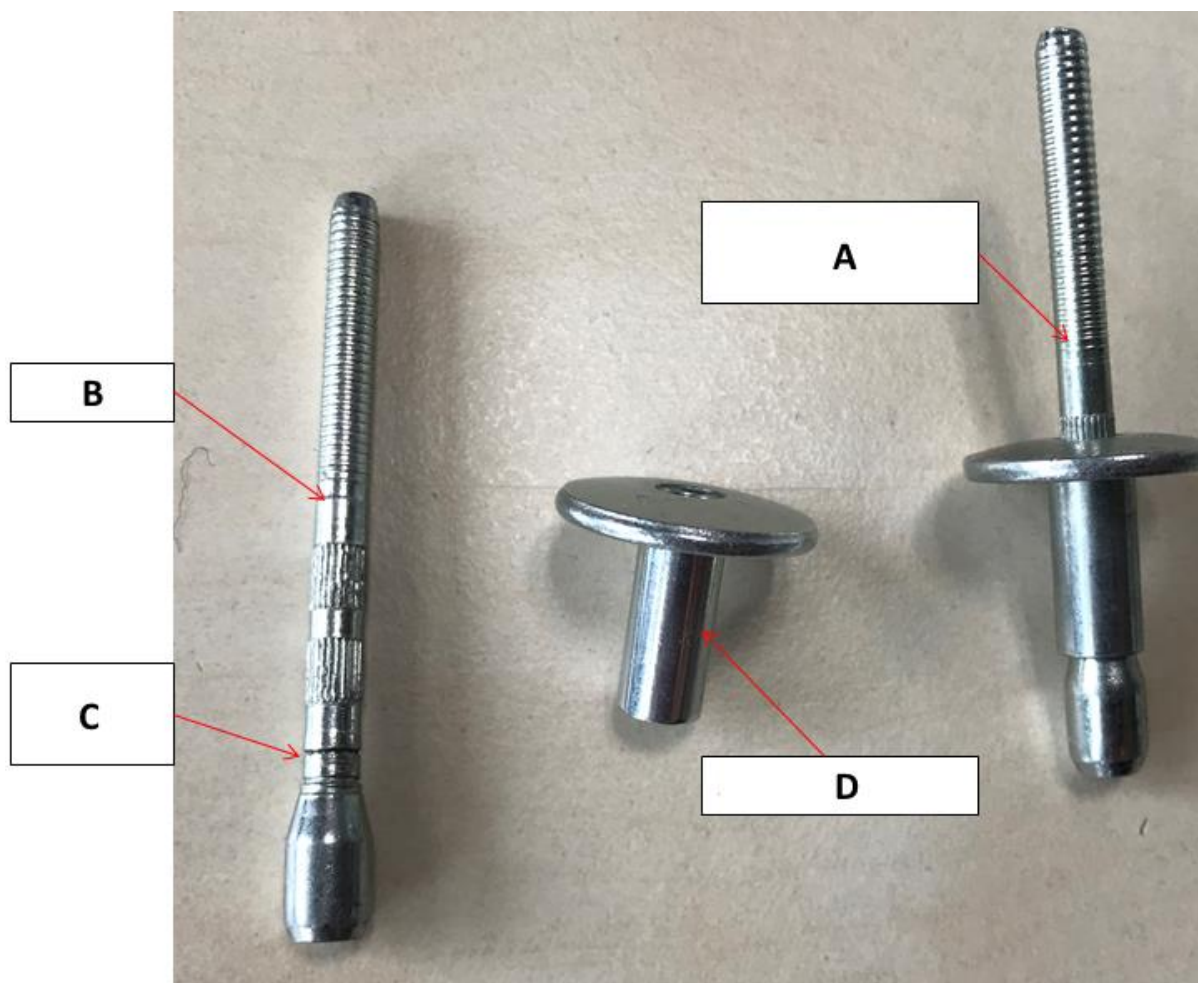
Os componentes de um rebite cego. A. Rebite cego montado, B. Mandril, C. Ponto de encaixe, D. Corpo do rebite cego. Fonte: TWI
